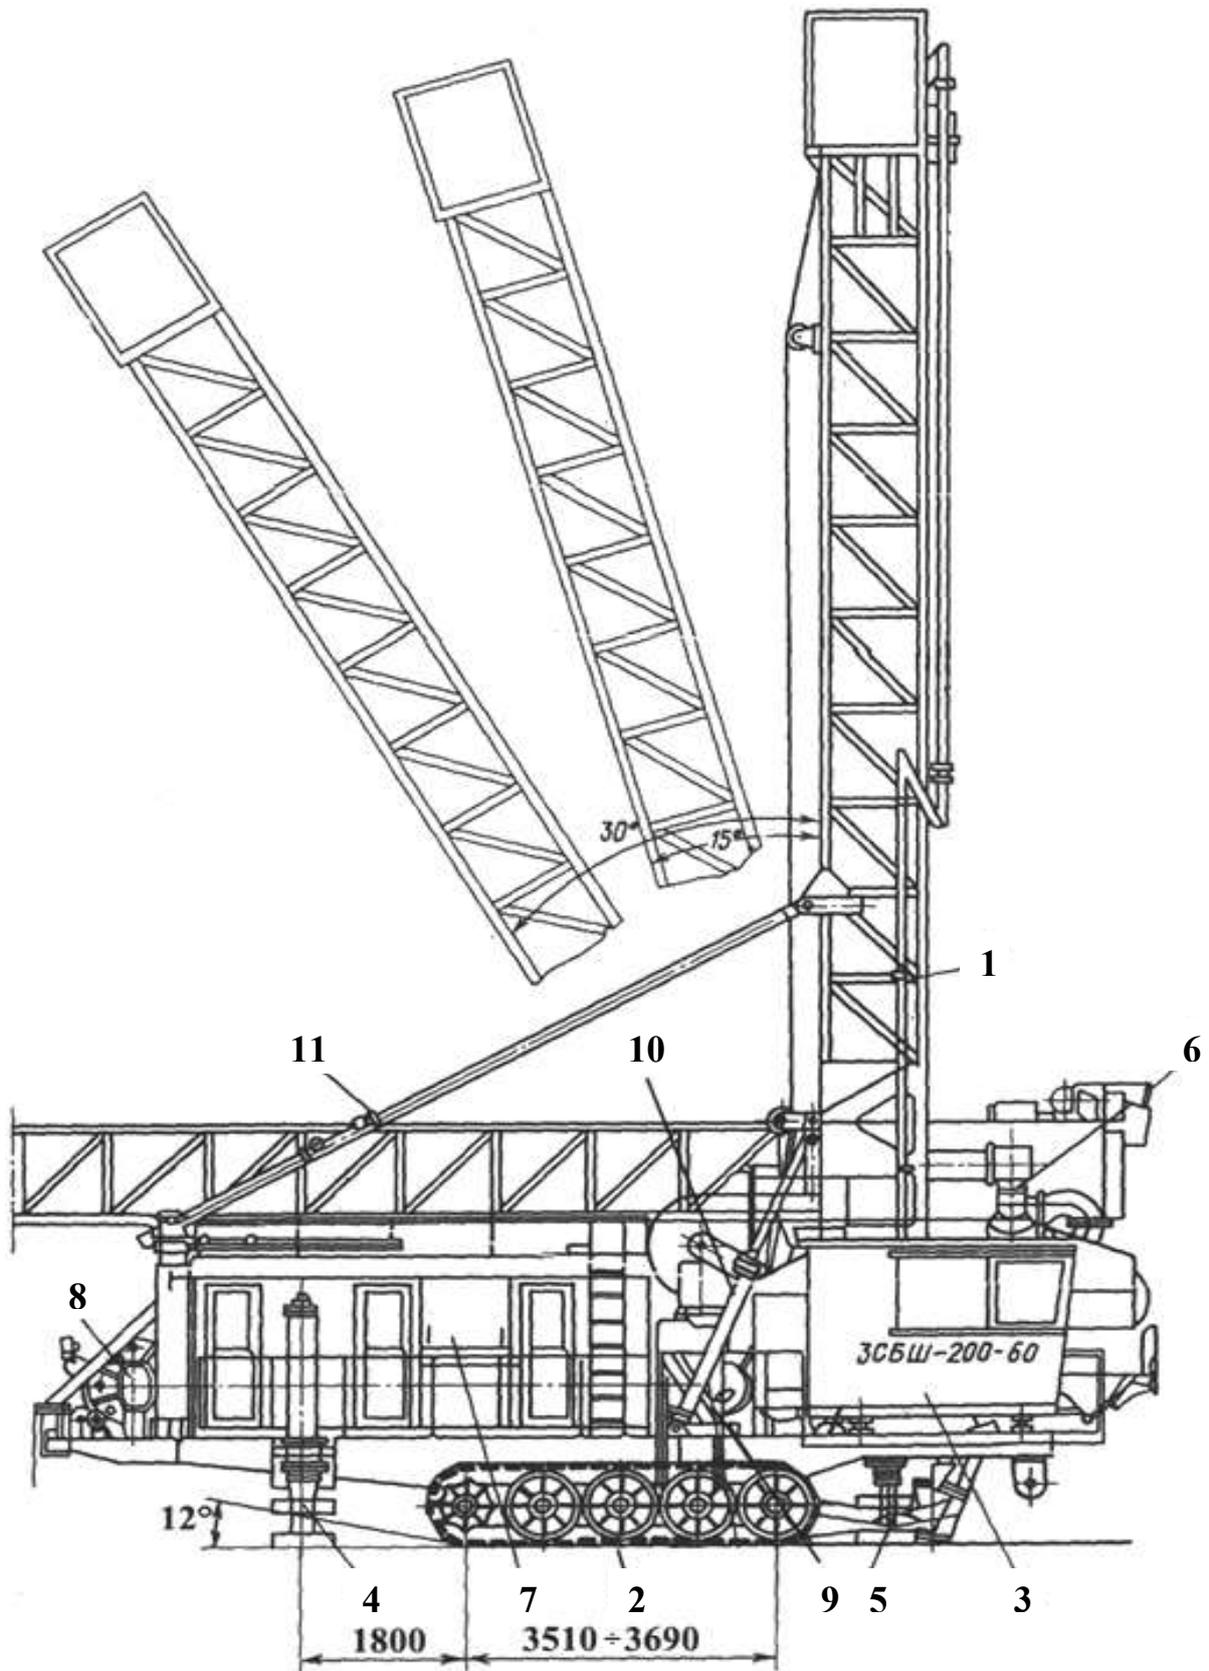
Общий вид карьерного бурового станка 3СБШ-200-60
